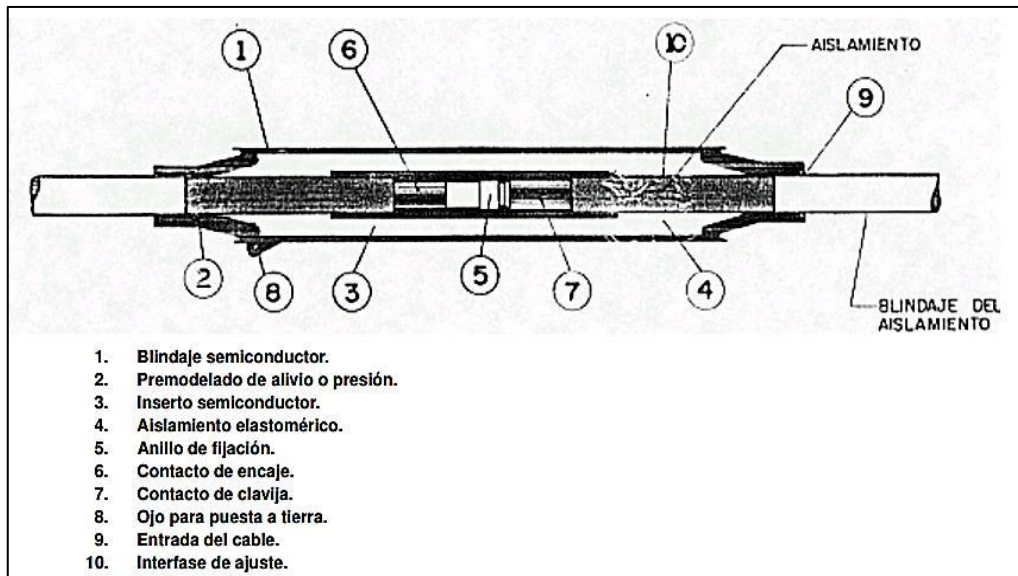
4 Detalle constructivo de empalmes encintados en cable monofásico con aislamiento extruido.
